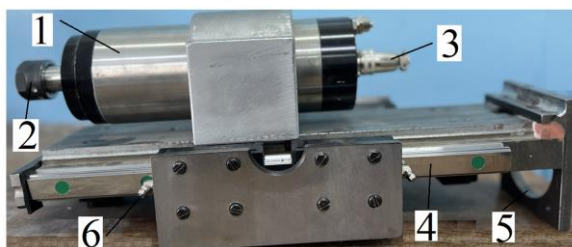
Общий вид крепления шпинделя фрезерного 3 – D станка.
